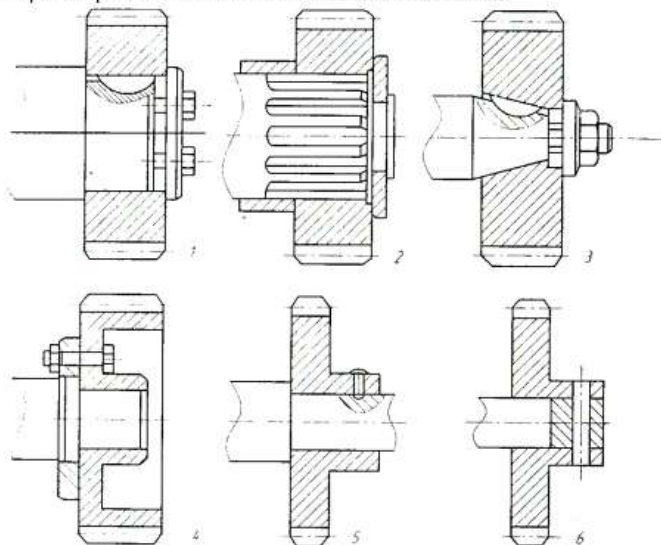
Способи установки і закріплення зубчастих коліс на валах: 1 – на циліндричній частині; 2 – на шлицевій частині; 3 – на конічній частині; 4 – на фланці; 5 – закріплення гвинтом; 6 – закріплення штифтом
